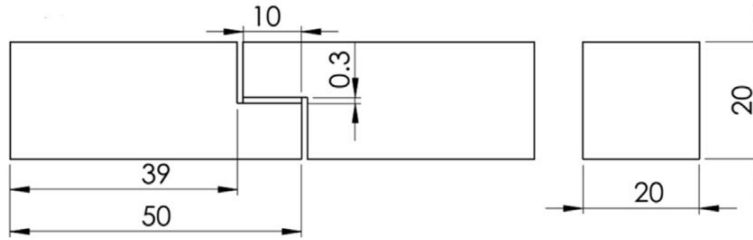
Géométrie de l'éprouvette TAST [42]
